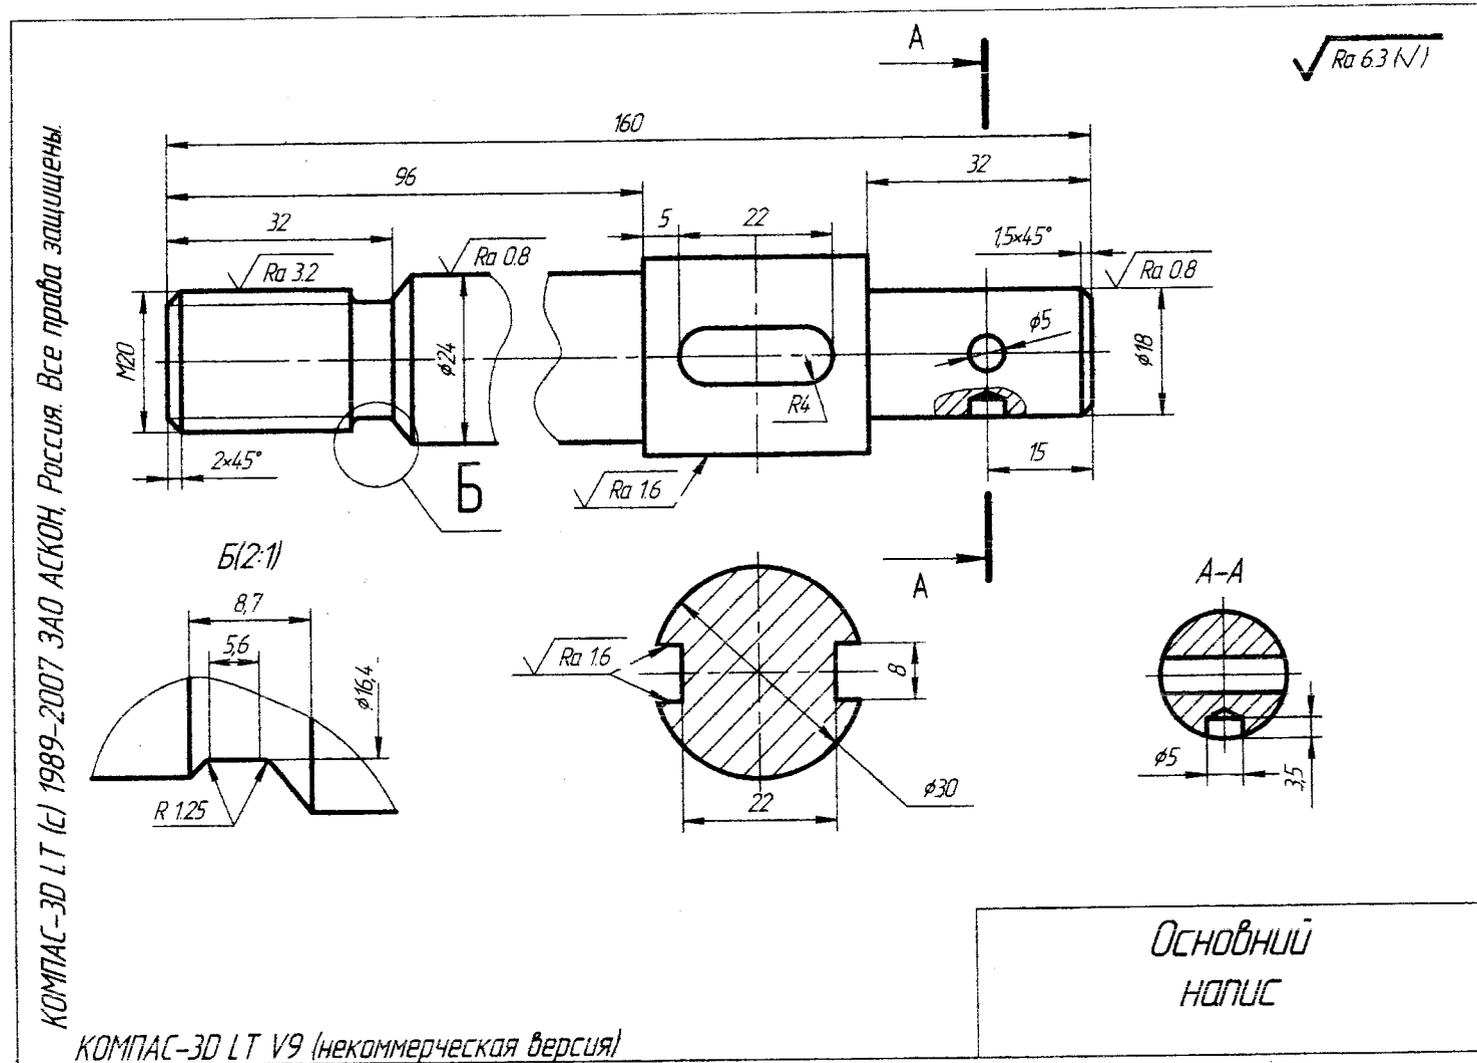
Зразок виконання робочого креслення вала з отворами та шпонковим пазом
